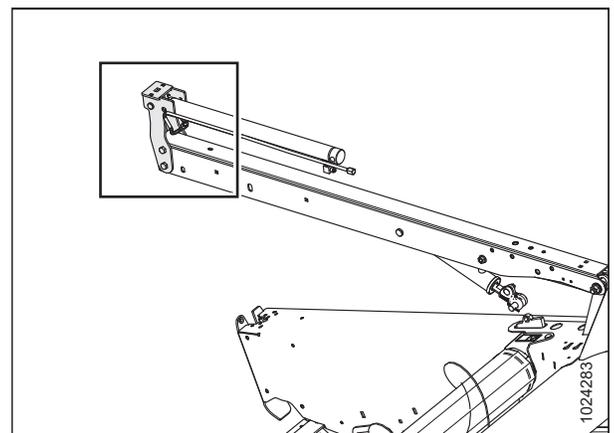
Rechter Haspelarm – Bauform für Mitte und links ähnlich
